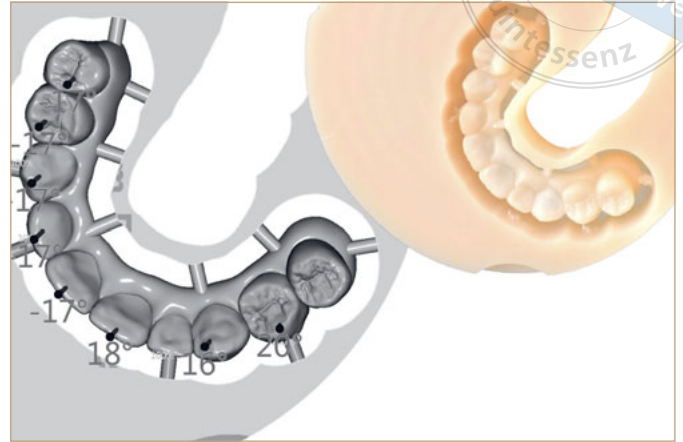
Die Fräsbahnberechnung berücksichtigt spezielle, einschneidige Fräser.
